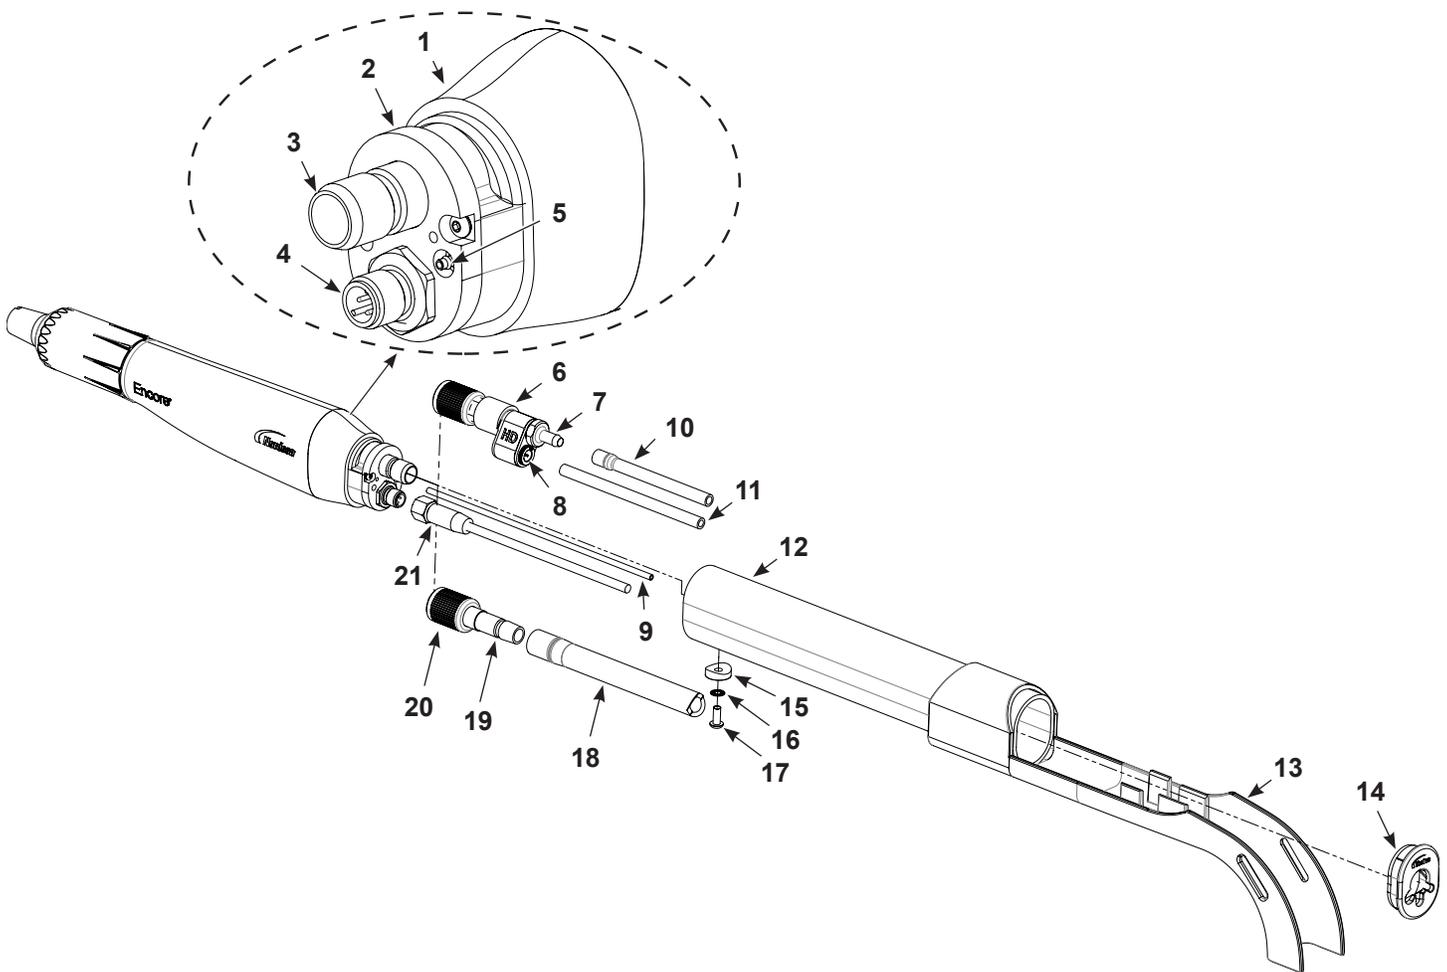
Collegamenti della pistola a spruzzo con montaggio su tubo
